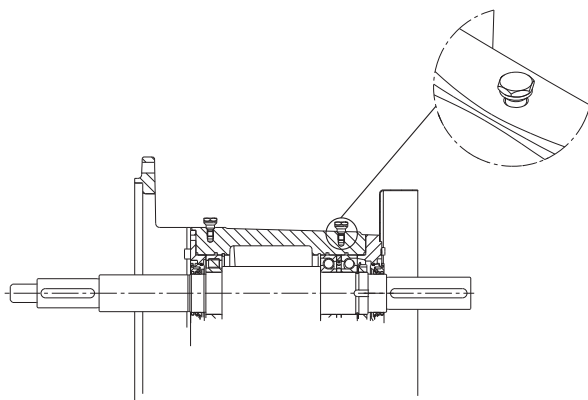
Корпус подшипника с местами для установки датчиков SPM
